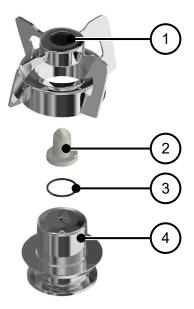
Baugruppe mit Gleitlager, Explosionsdarstellung
